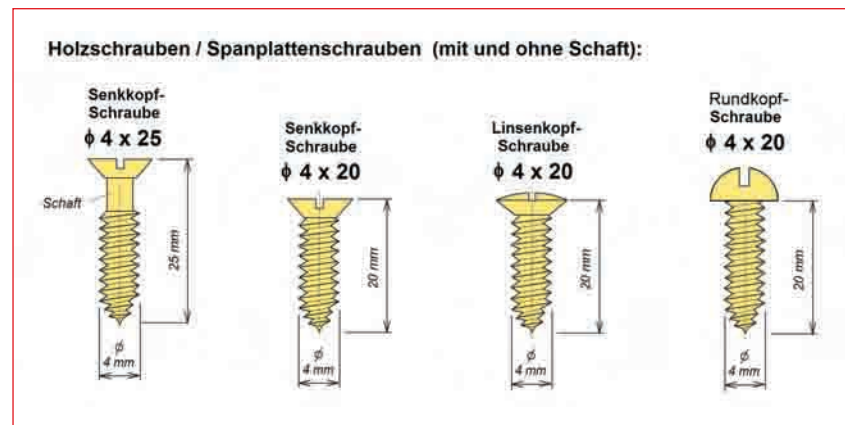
Auch aus der Holzschraubenbezeichnung geht hervor, wie dick und wie lang die Schraube ist.
